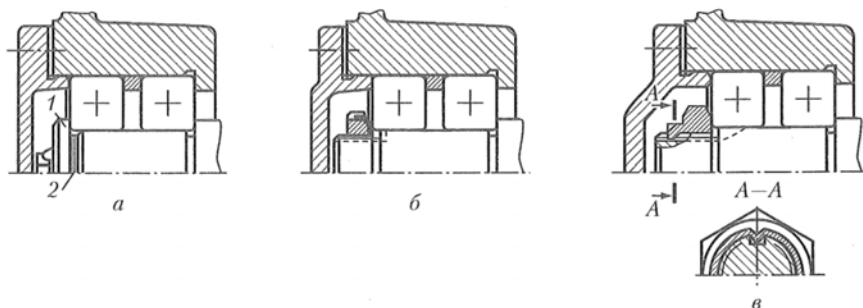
Способы регулирования зазоров в подшипниках перемещением внутреннего кольца: а – торцевой шайбой 1; б – шлицевой гайкой; в – винтом с деформируемым бортом
